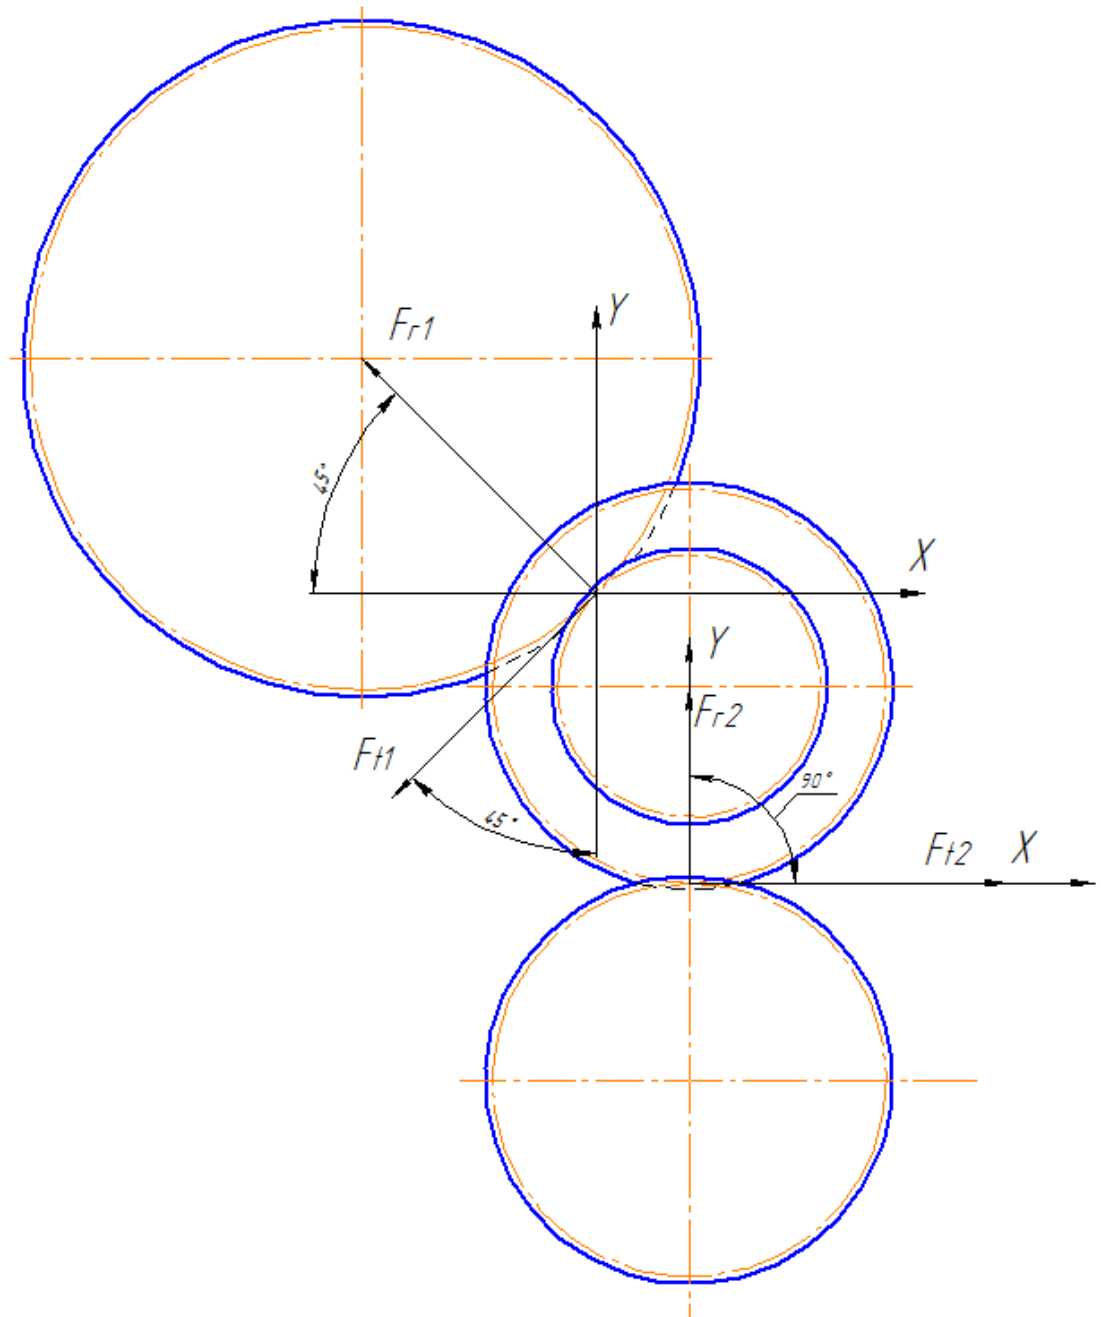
Компоновка валів та зубчатих коліс у коробці верстату
